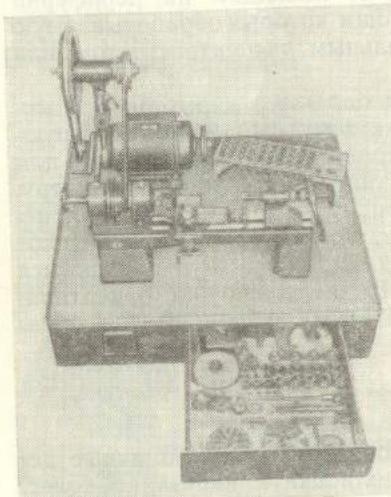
Универсальный токарный станок «Фаворите» (Швейцария)
